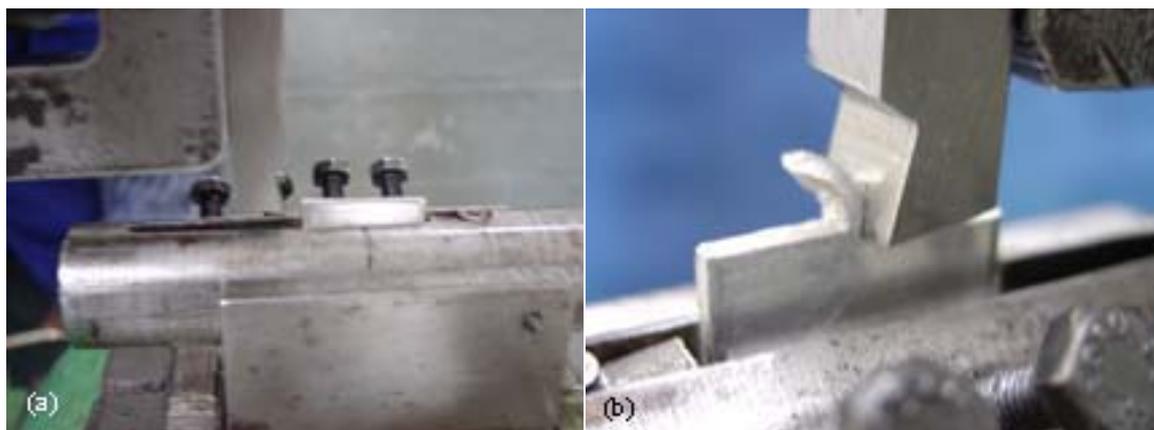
Fotografias mostram a ferramenta antes (a) e depois (b) do cavaco ser formado sobre a amostra montada e fixa ao suporte móvel.
